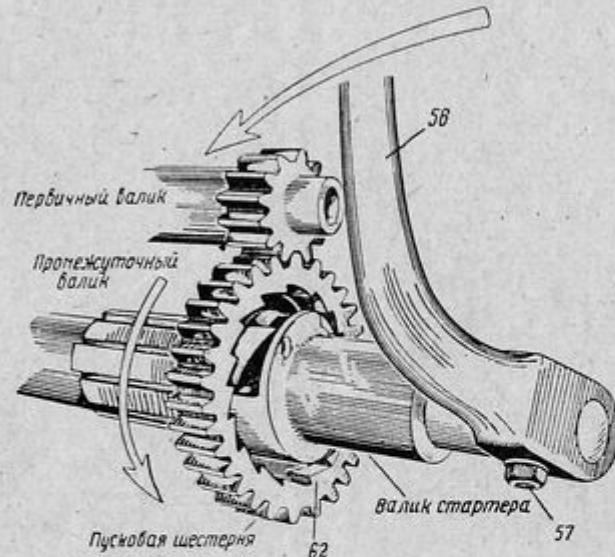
Стартерный механизм коробки перемены передач Л-300:
